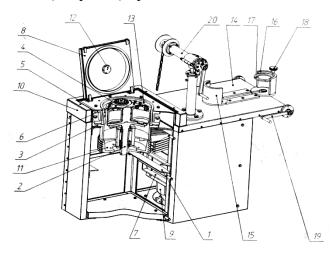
Внешний вид и устройство механоактиватора АГО-3
